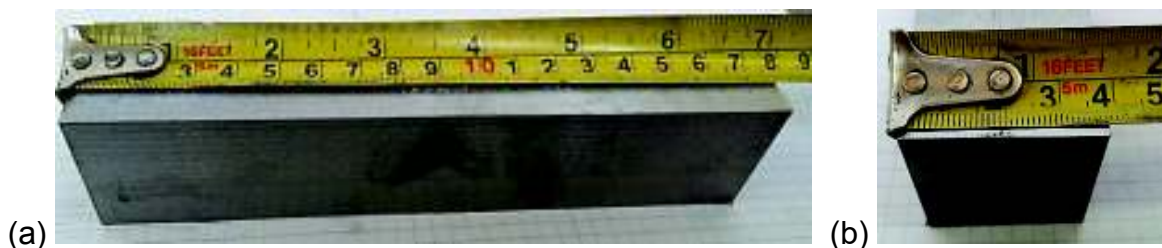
Dimensiones del bloque para ensayo de soldabilidad
